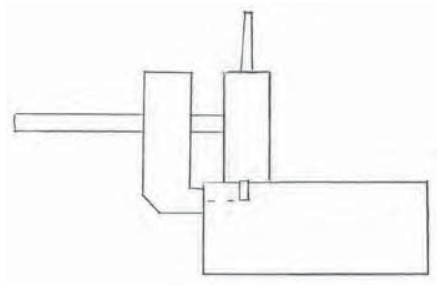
Den fasta nothyveln inställd på falsens breddmått 31 mm och det fasta djupet 12 mm ger ett mått på 31 x 12 mm.
